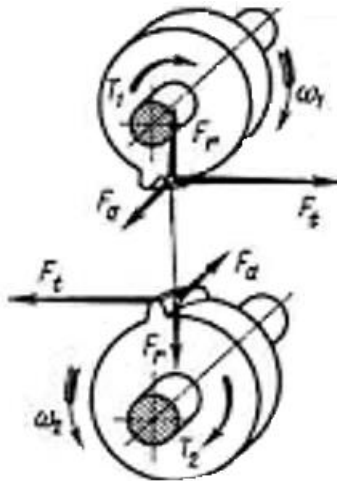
Схема сил діючих в циліндричній косозубій передачі
